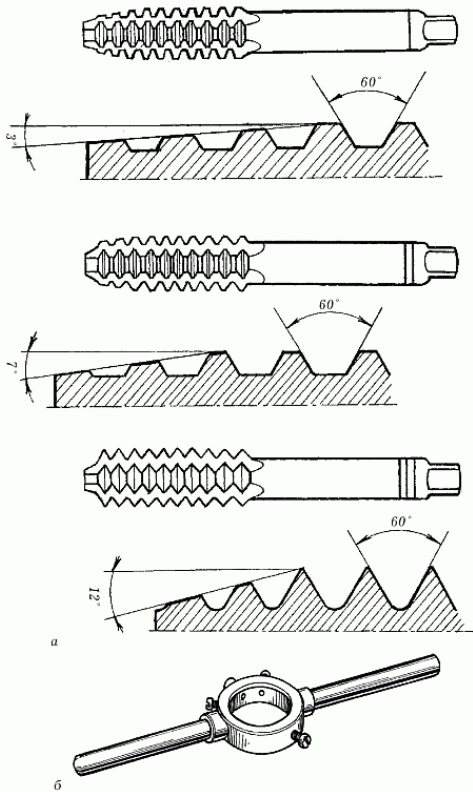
Инструменты для нарезания внутренней резьбы: а – метчики; б – вороток
